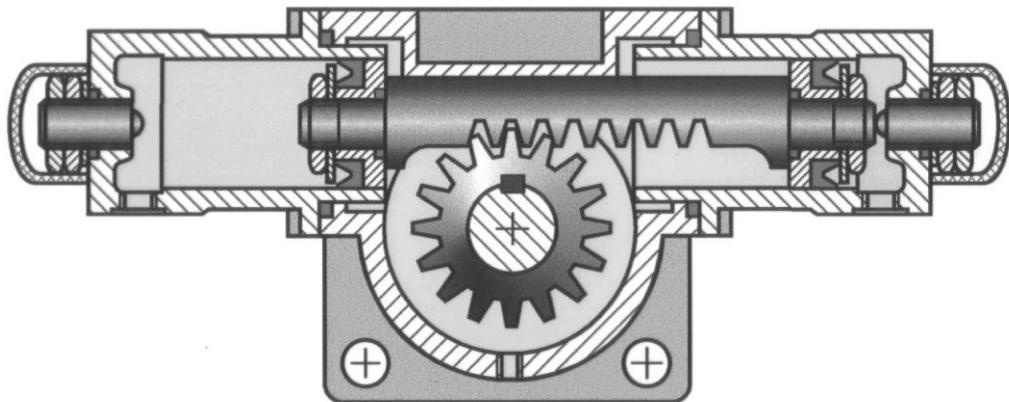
Гидродвигатель поворотного действия поршневого типа
